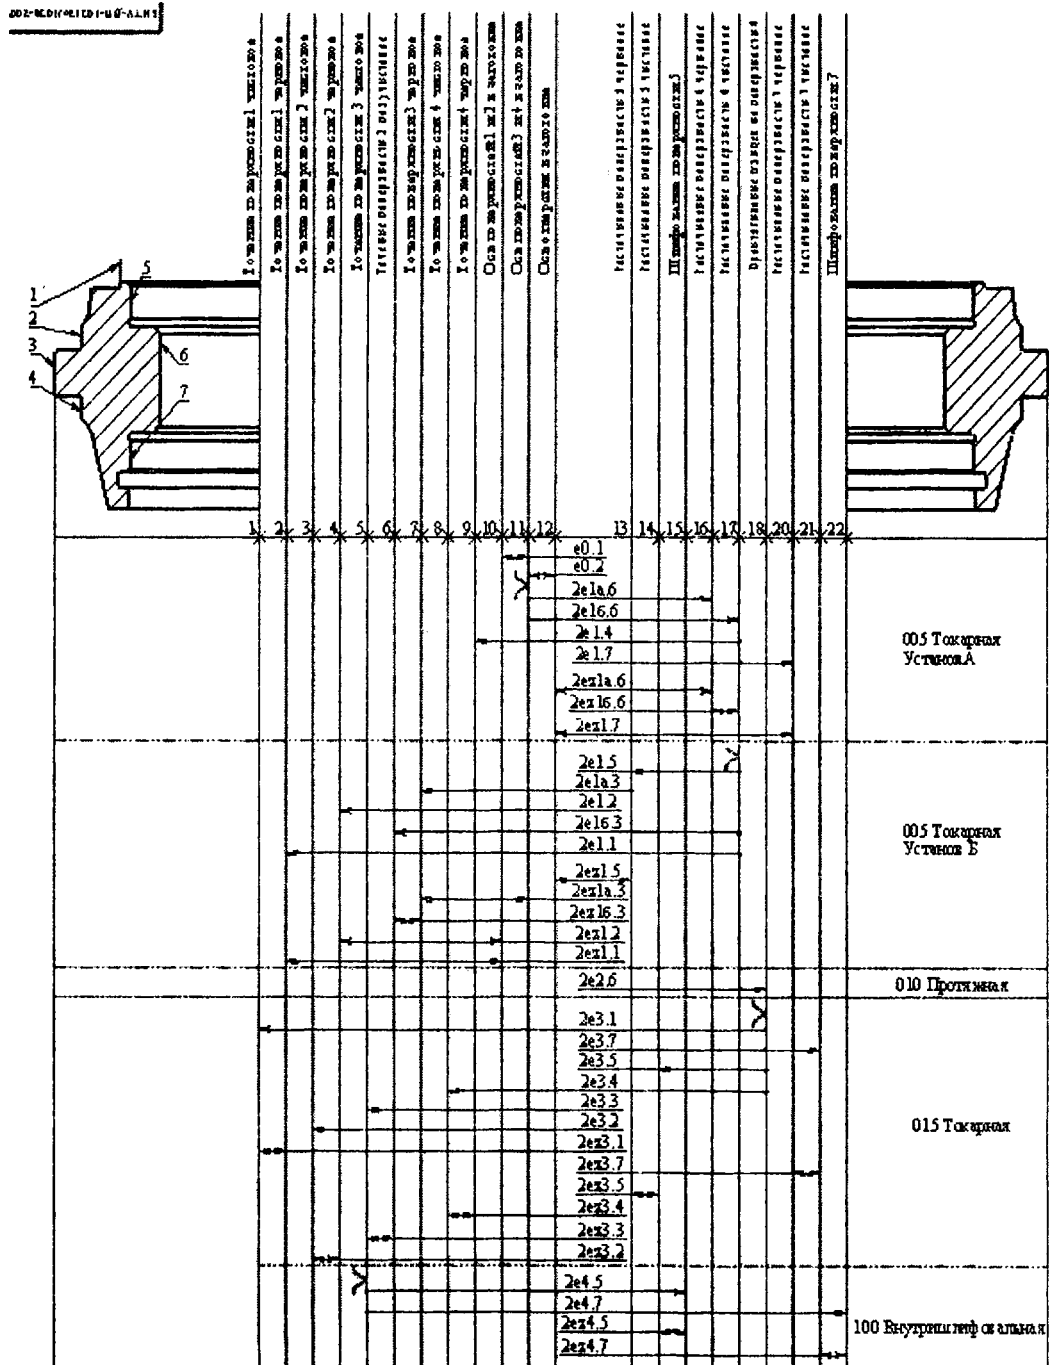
Размерная схема техпроцесса обработки детали «Шестерня»
